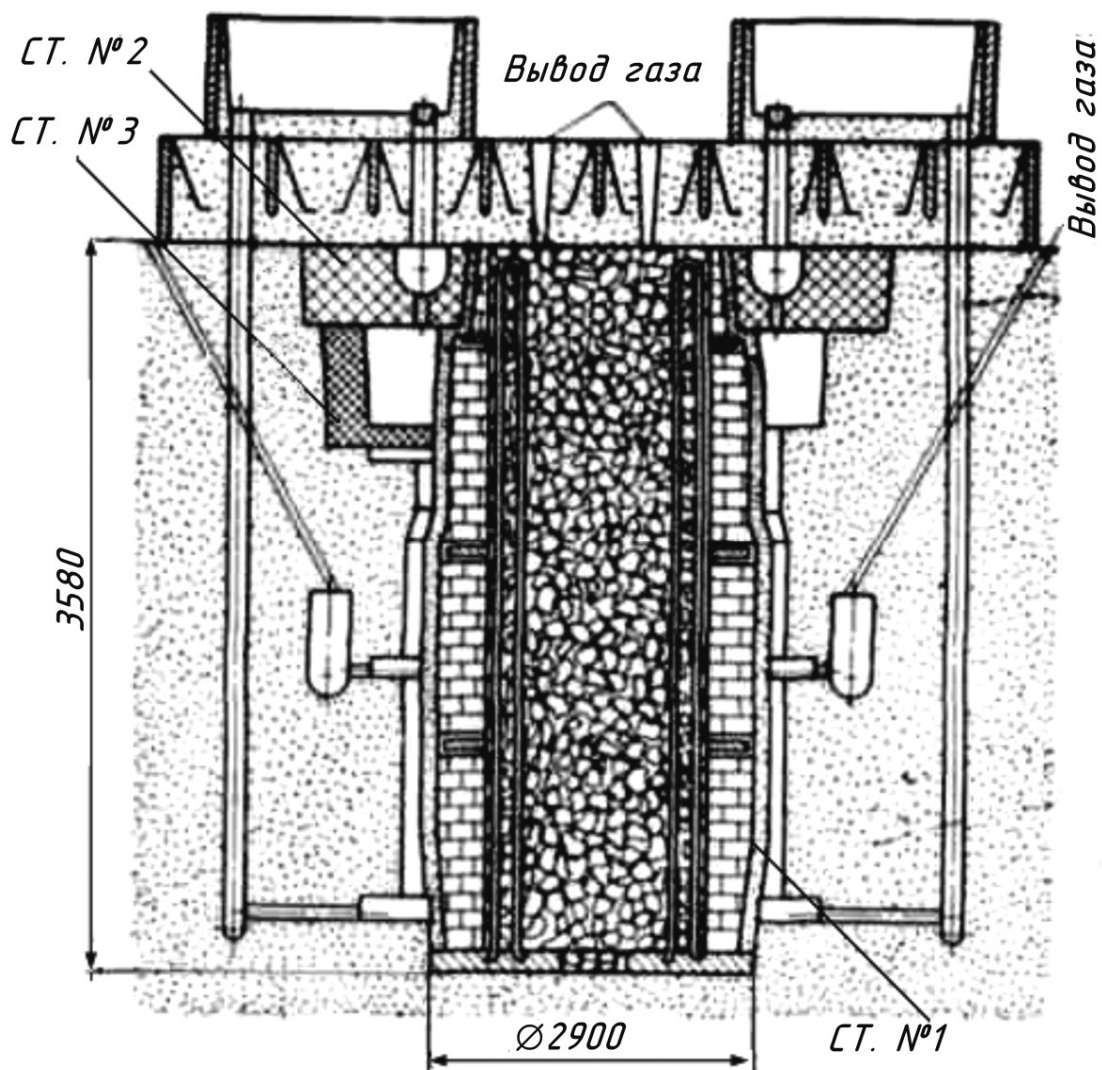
Форма отливки нижней части парового цилиндра в собранном виде
